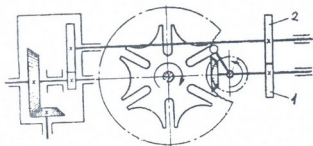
Схема привода главного транспортера агрегата БТГ
